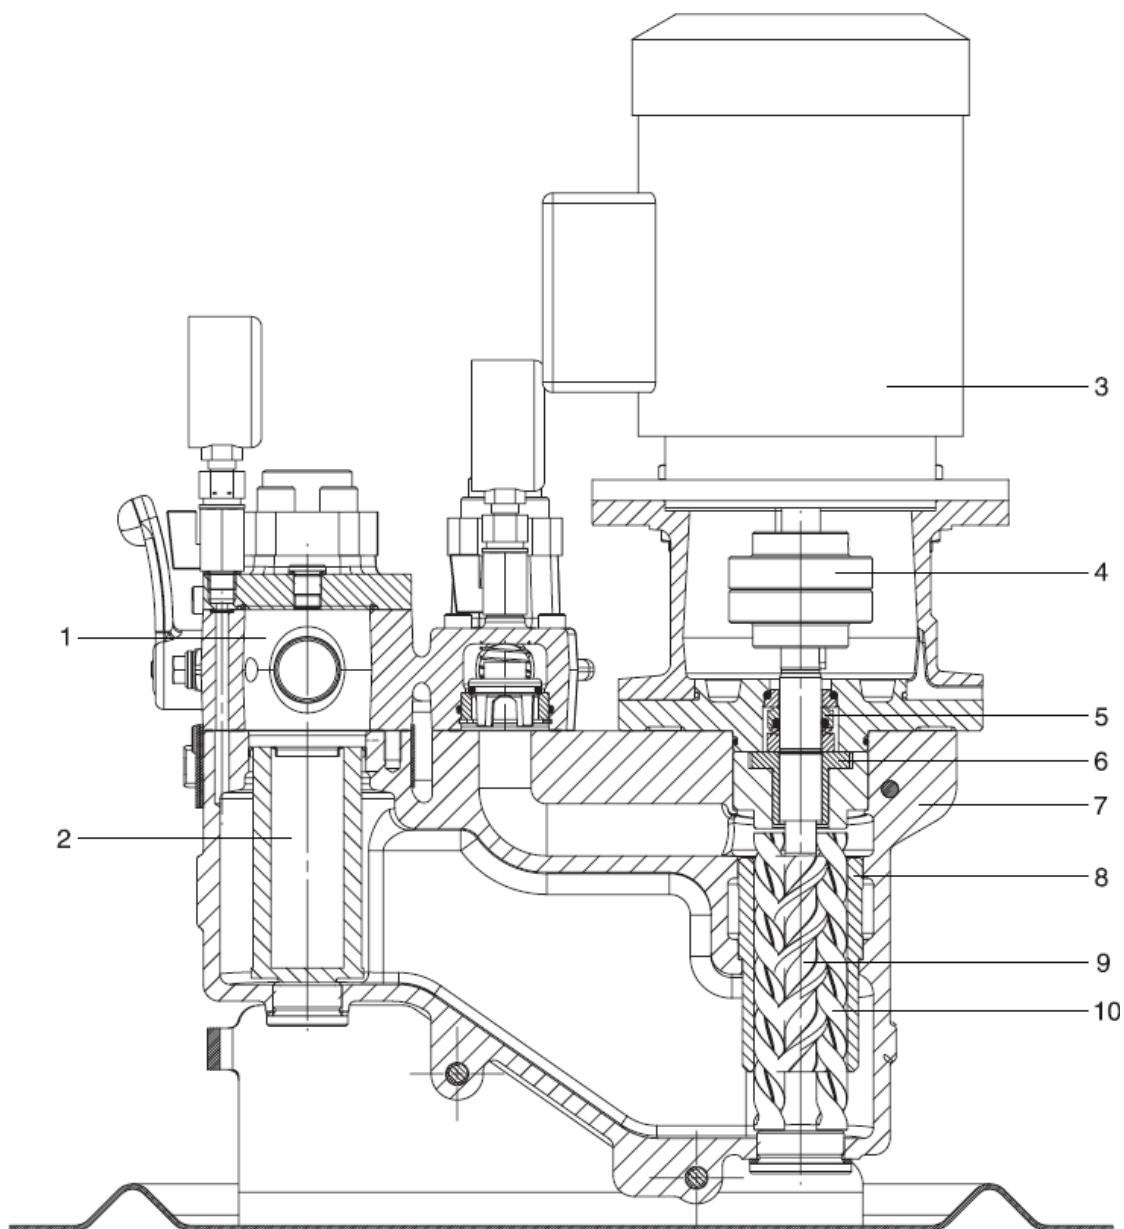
Конструкция сдвоенного агрегата с фильтром
